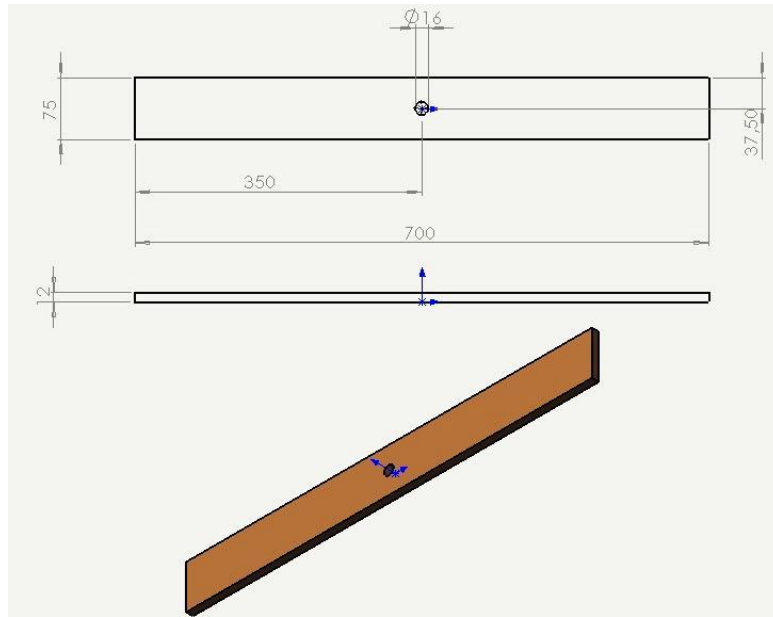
Dimensiones expresadas en milímetros y figura en 3D del soporte de la tuerca del Eje X
